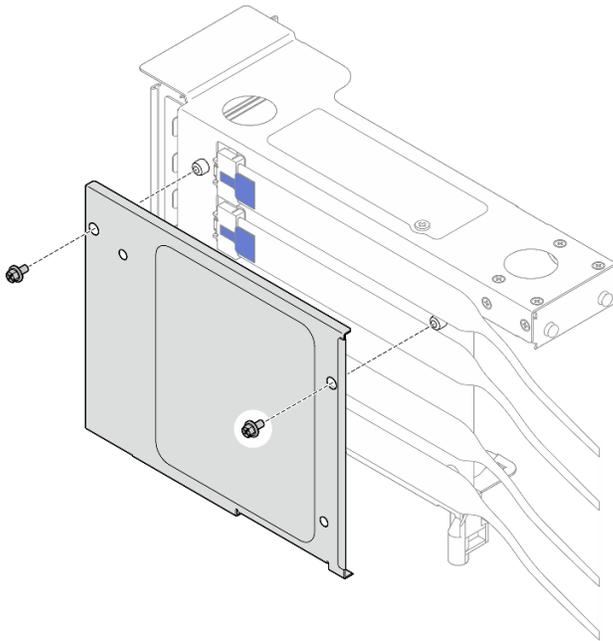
Installation du cache sur le boîtier de la carte mezzanine
